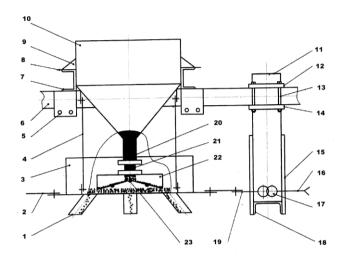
Вибрационный высевающий аппарат со стабилизатором уровня семян: 1 - наконечник семяпровода; 2 - шатун; 3 - высевающее устройство; 4 - гибкая подвеска; 5 - болтовое соединение; 6 - рама; 7 - кронштейн; 8 - пластина; 9 - косынка; 10 - бункер; 11 - вертикальный кронштейн; 12 - верхняя накладка; 13 - болтовое соединение; 14 - нижняя накладка; 15 - косынка кронштейна; 16 - шатун левого высевающего устройства; 17 - привод; 18 - горизонтальная полка; 19 - шатун левого высевающего устройства; 20 - патрубок цилиндрический; 21 - трубка цилиндрическая; 22 - стабилизатор уровня семян; 23 - корпус стабилизатора
